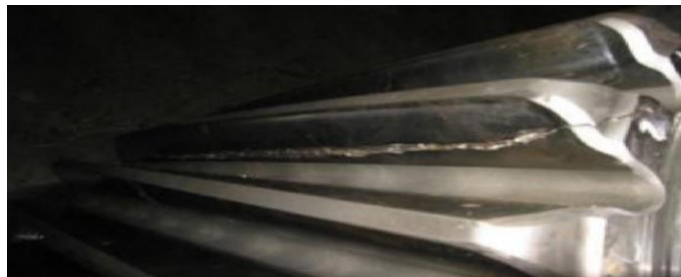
Fissuration ou cracks "Engrenages". [15]
